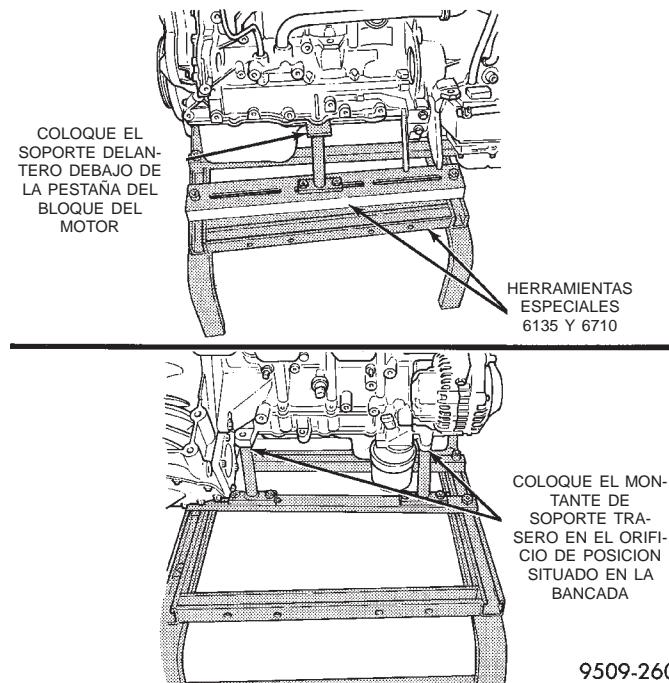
Emplazamiento de los soportes de montantes del armazón del motor
